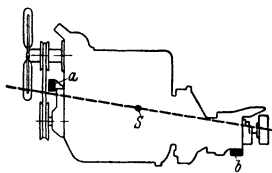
Schwebende Aufhängung des Motor-Getriebelocks nach Mecano. Schwerpunkt *S*, Gummilager *a* und U-förmiges Gummilager *b*.
